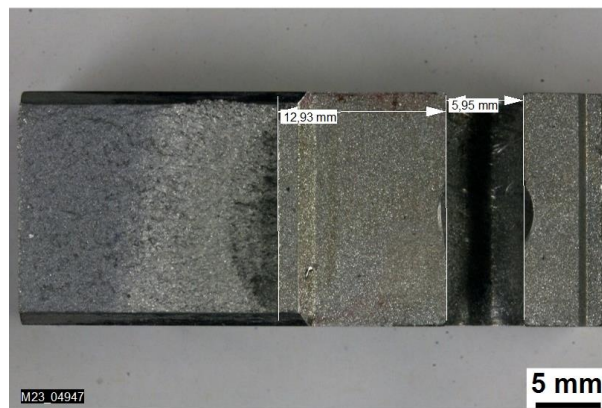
Probe 5.5 Makroaufnahme Probenhälfte mit ausgemessener Länge von Lastangriffslinie bis zur erodierten Kerbe
